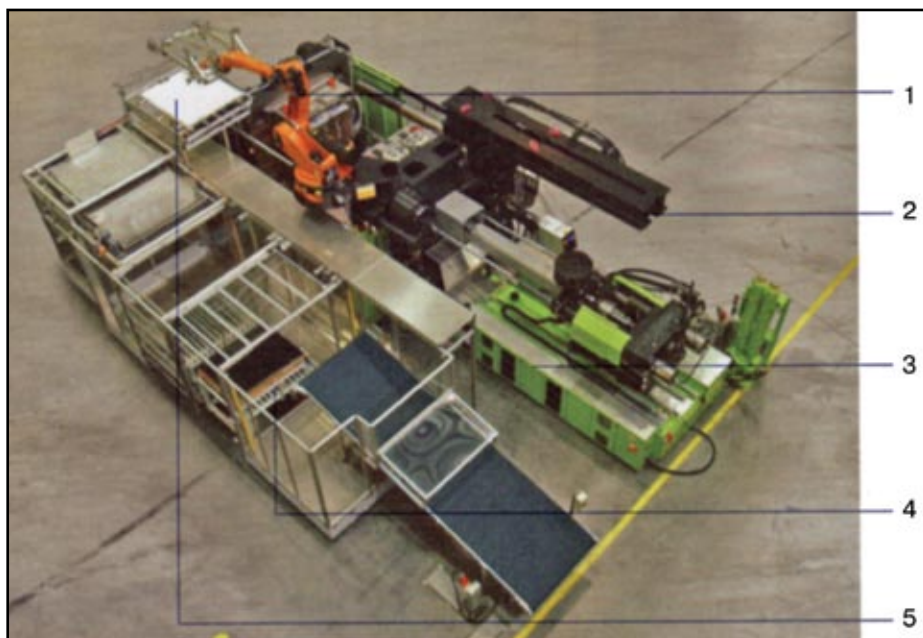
Производственный модуль на базе ТПА марки ENGEL DUO 7050/1700 Tecomelt: 1 - гибкий робот для манипуляций с текстильными заготовками и готовыми деталями; 2 - устройство для облегчения монтажа и демонтажа больших пресс-форм; 3 - аккумулятор давления для увеличения скорости литья; 4 - периферийная станция для своевременной подготовки и подачи текстильных заготовок и удаления готовых деталей; 5 - станция предварительного подогрева текстильных заготовок (источник: Engel)
